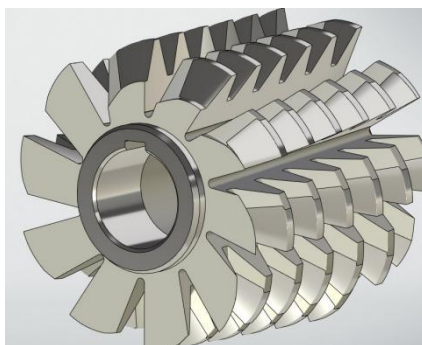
Пример червячной фрезы для эвольвентного модульного колеса
